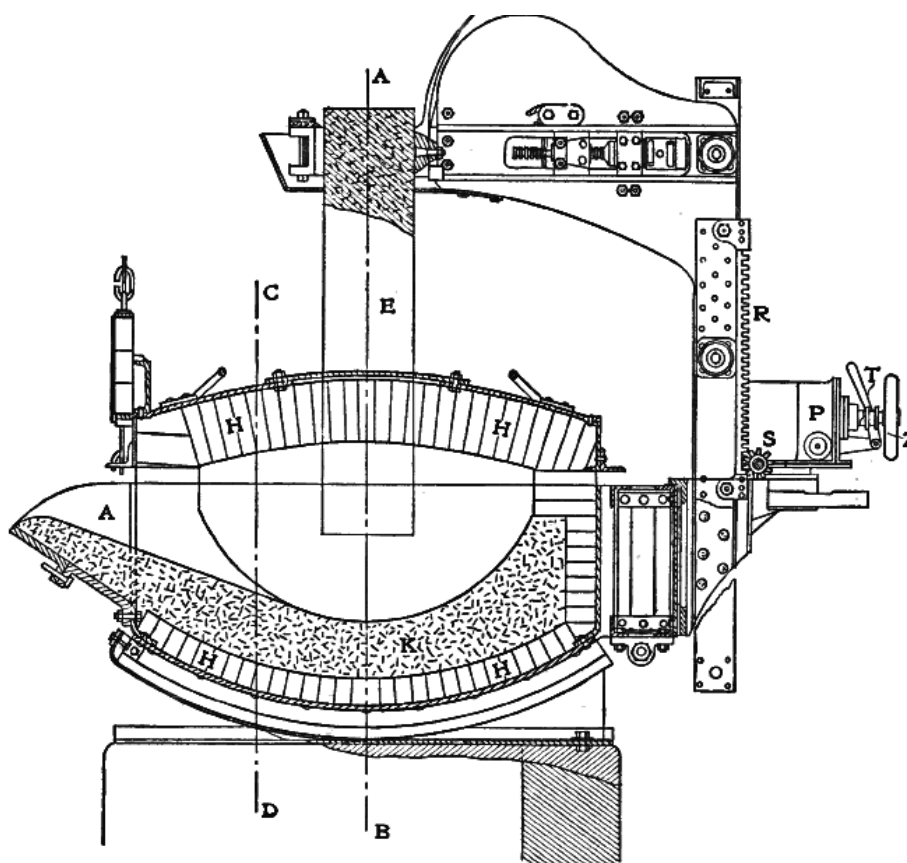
Схематичний поперечний переріз через дугову піч Heroult
